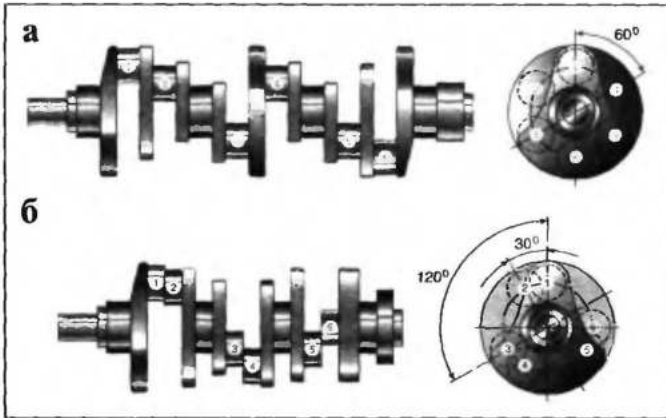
Коленчатые валы V-образных 6-цилиндровых двигателей: а — при угле развала цилиндров 75° ; б — при угле развала цилиндров 90° — отсутствие щек между парами шатунных шеек позволяет существенно сократить длину двигателя (AUDI)
